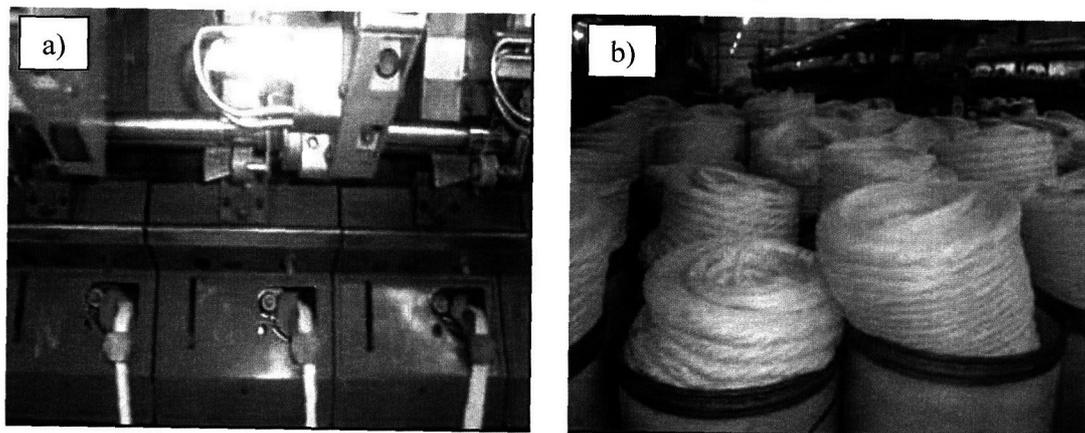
a) Máquina denominada de carda e b) e latas de fitas de carda.
